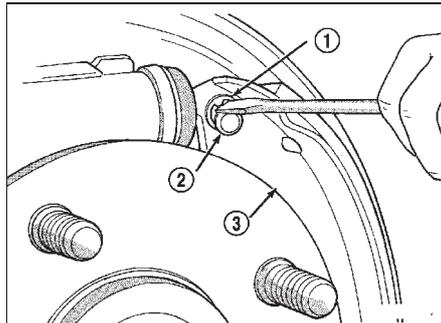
Стопорное кольцо пальца рычага стояночного тормоза. 1 - стопорное кольцо, 2 - палец рычага стояночного тормоза, 3 - рычаг стояночного тормоза.
